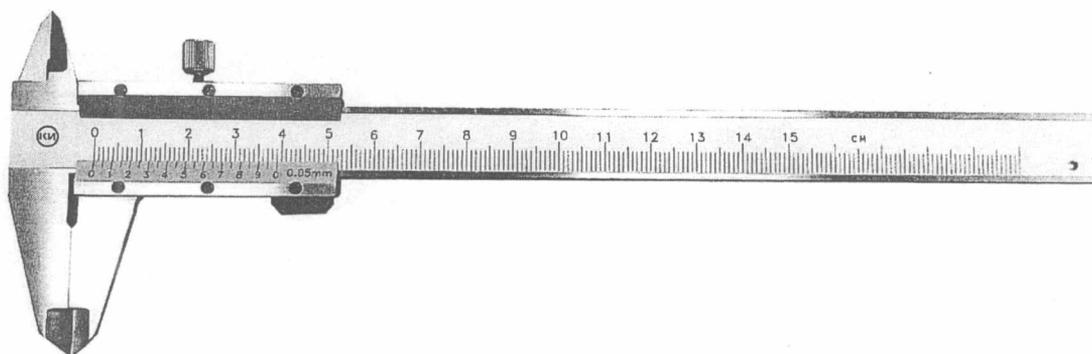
Общий вид штангенциркулей типа ШЦ-I
